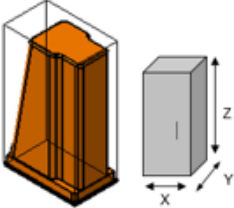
Zobrazení umístění držáků pro elektrody
